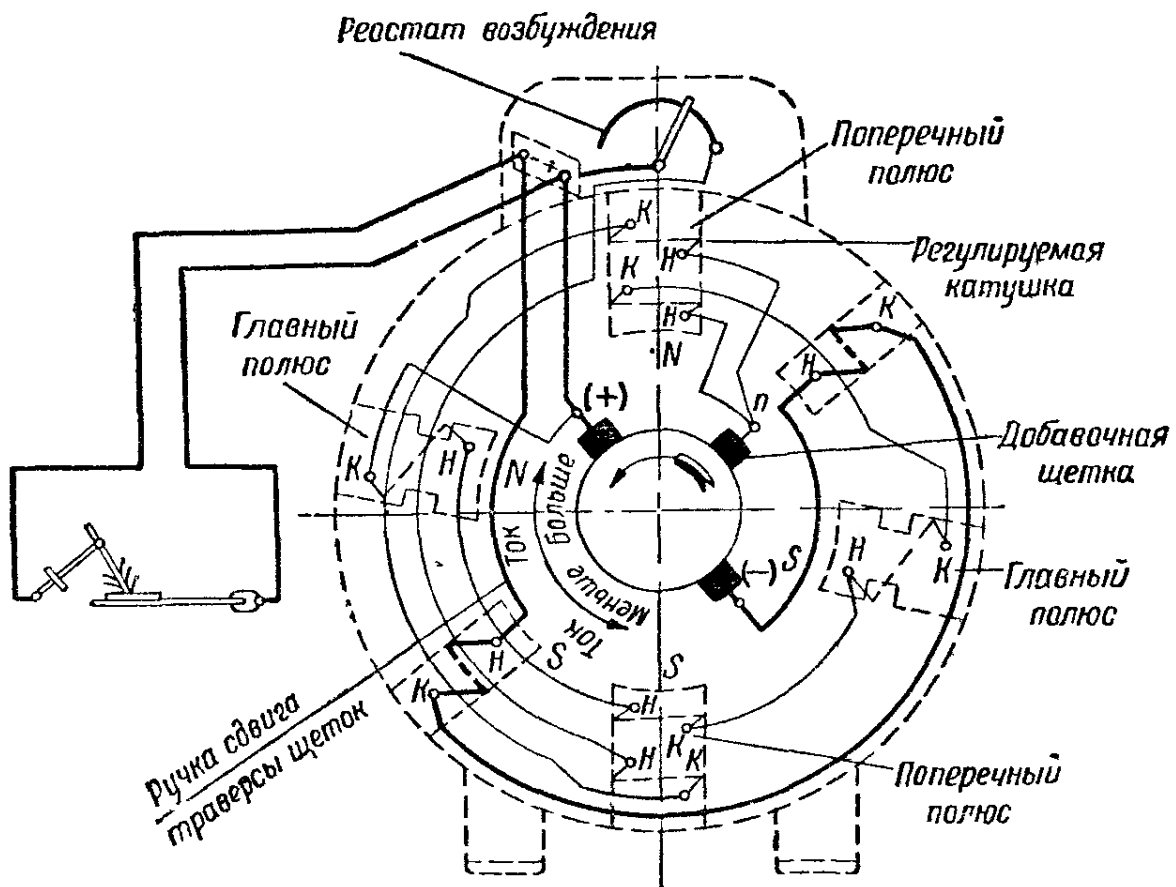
Схема обмоток и включения в сварочную цепь генератора СМГ-2 (вид со стороны коллектора)
